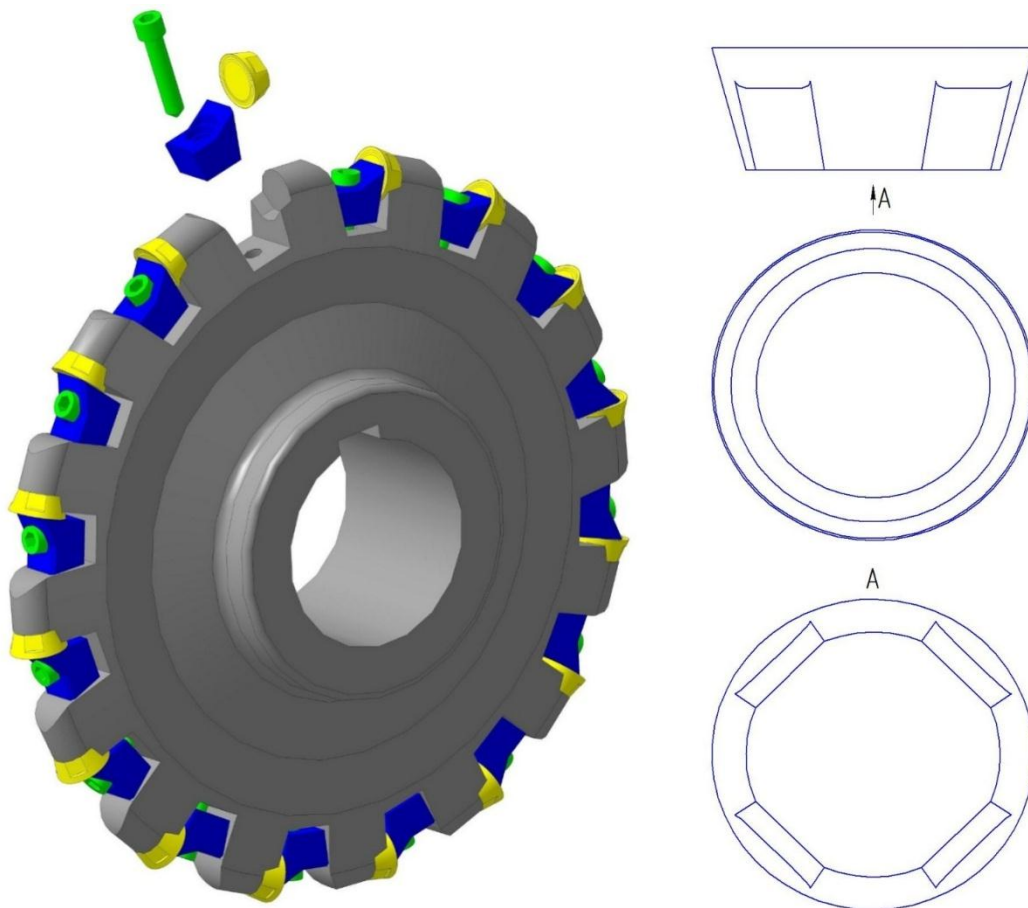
Разработанная конструкция сборной дисковой фрезы с круглыми усеченными под паз пластинами
